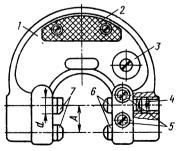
Скоба гладкая, регулируемая, с двумя подвижными вставками и двумя неподвижными пятками:
